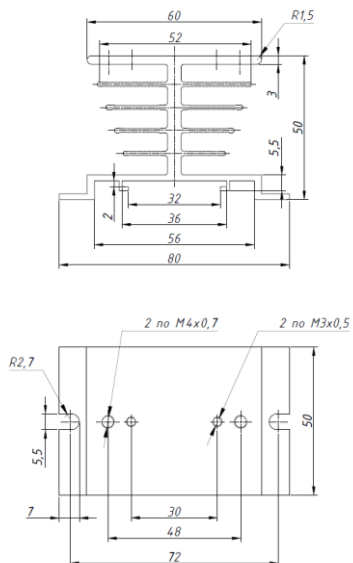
габаритные и установочные размеры радиатора РТР060
